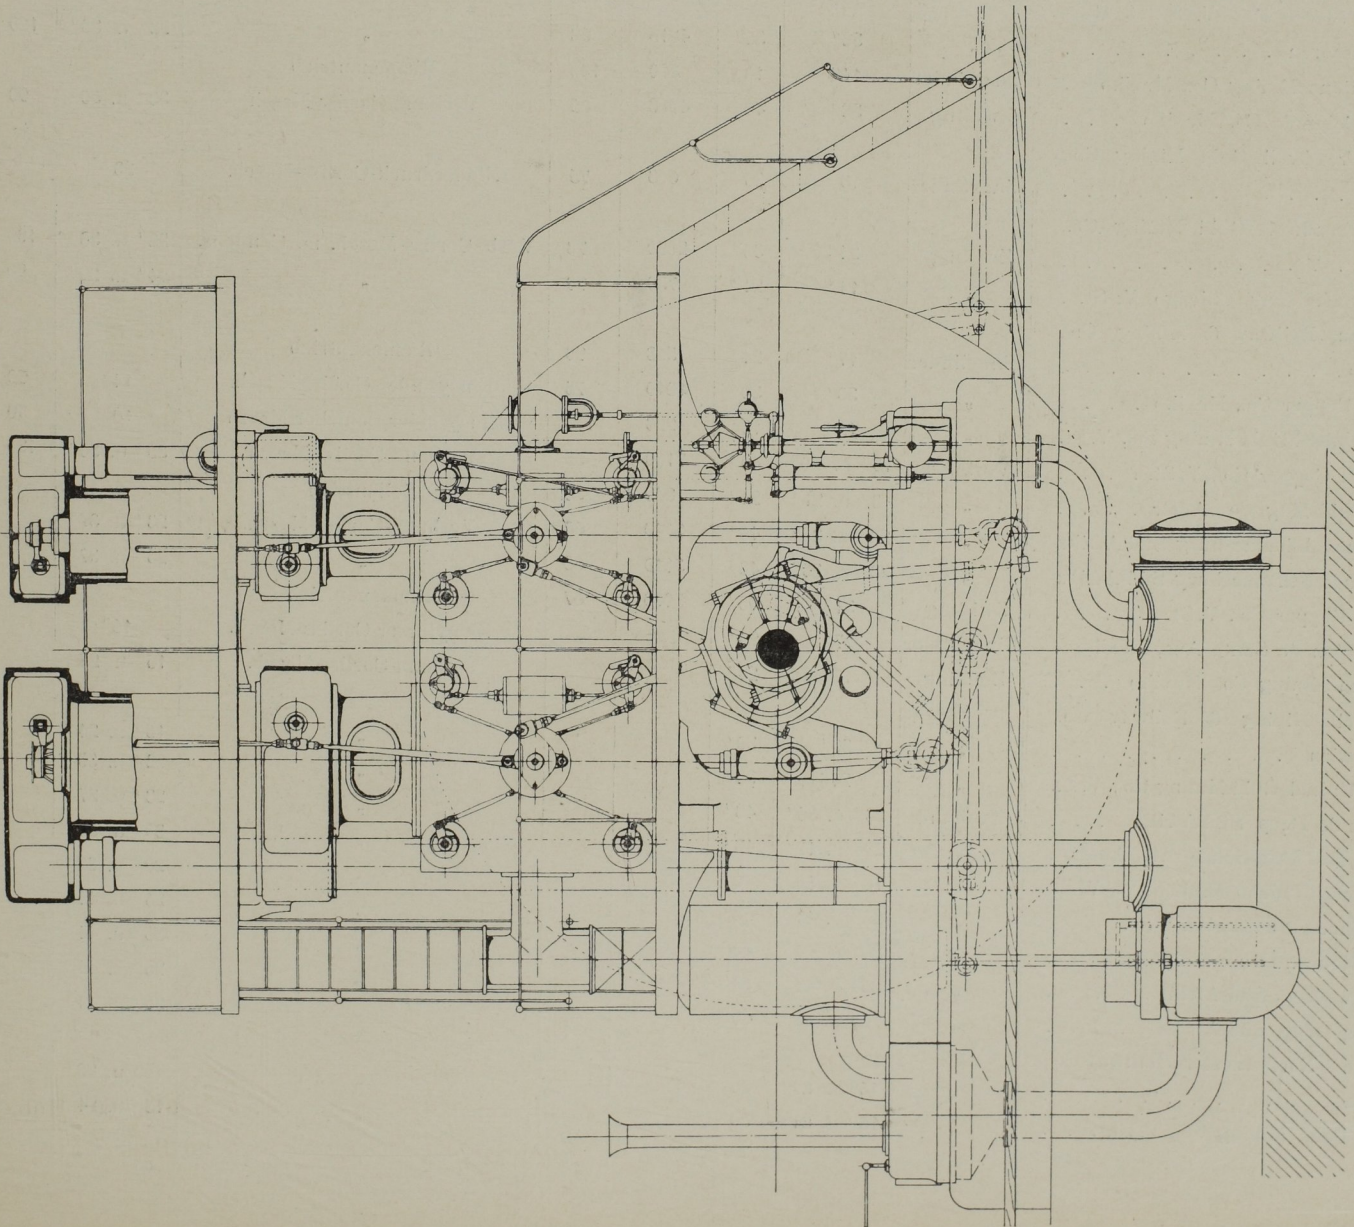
Seitenansicht der Maschine. Massst. 1:48.
